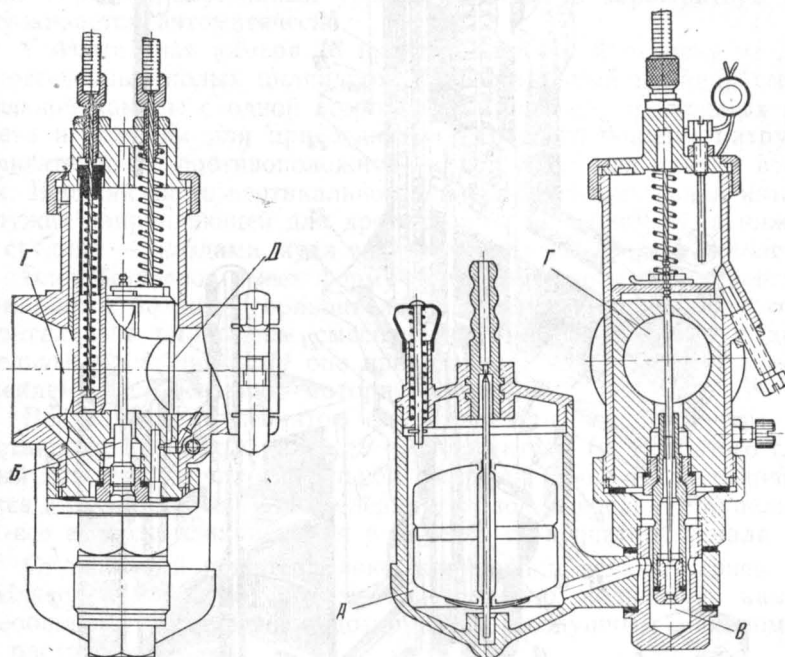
Карбюратор К-28: А — поплавковая камера; Б — кольцевая камера; В — промежуточный топливный колодец; Г — смесительная камера; Д — диффузор.
